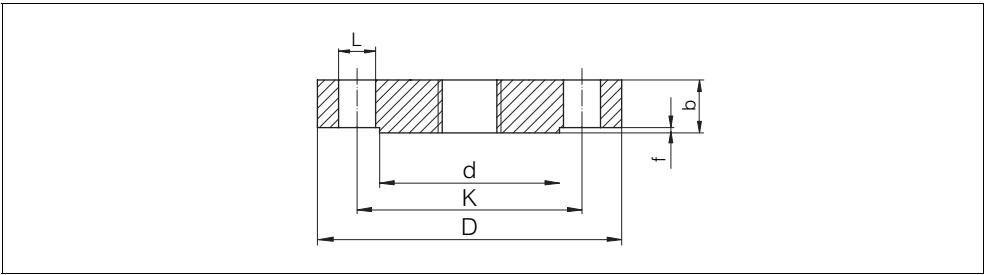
Maße - JIS-Flansch (Regular Flange)
